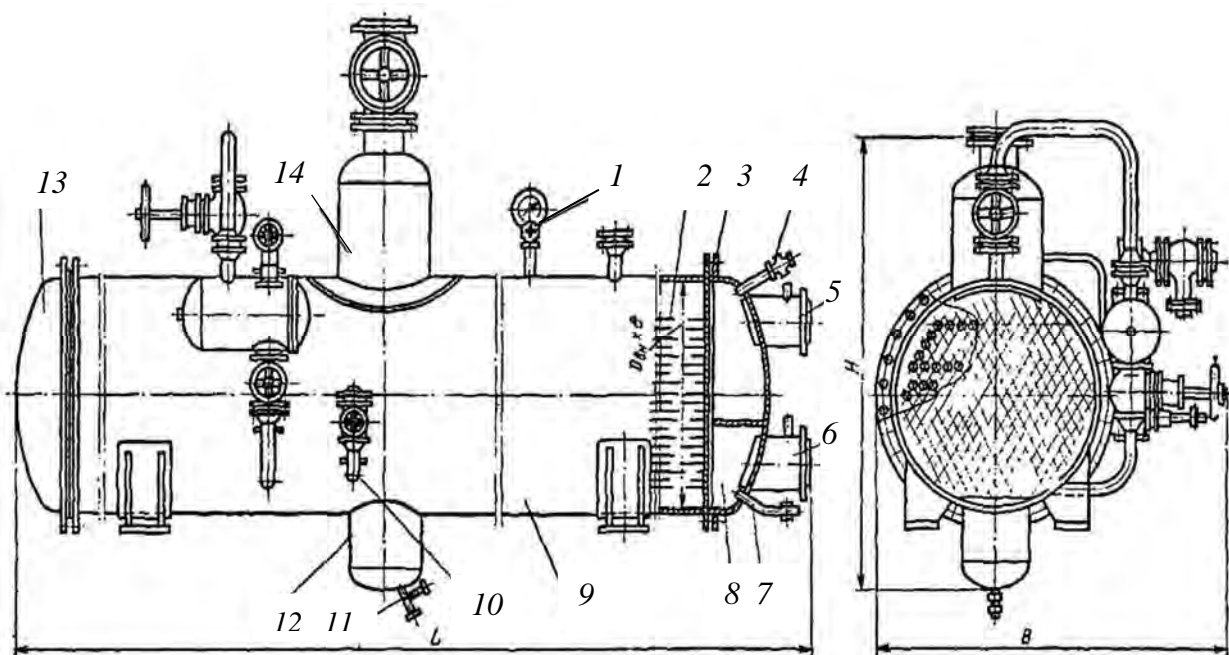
Аммиачный кожухотрубный испаритель затопленный: 1 – манометр; 2 – трубы; 3 – трубная решетка; 4 – спуск воздуха; 5, 6 – патрубки для входа и выхода рассола; 7 – слив рассола; 8, 13 – крышки; 9 – корпус; 10 – вход жидкого аммиака; 11 – спуск масла; 12 – отстойник; 14 – сухопарник
